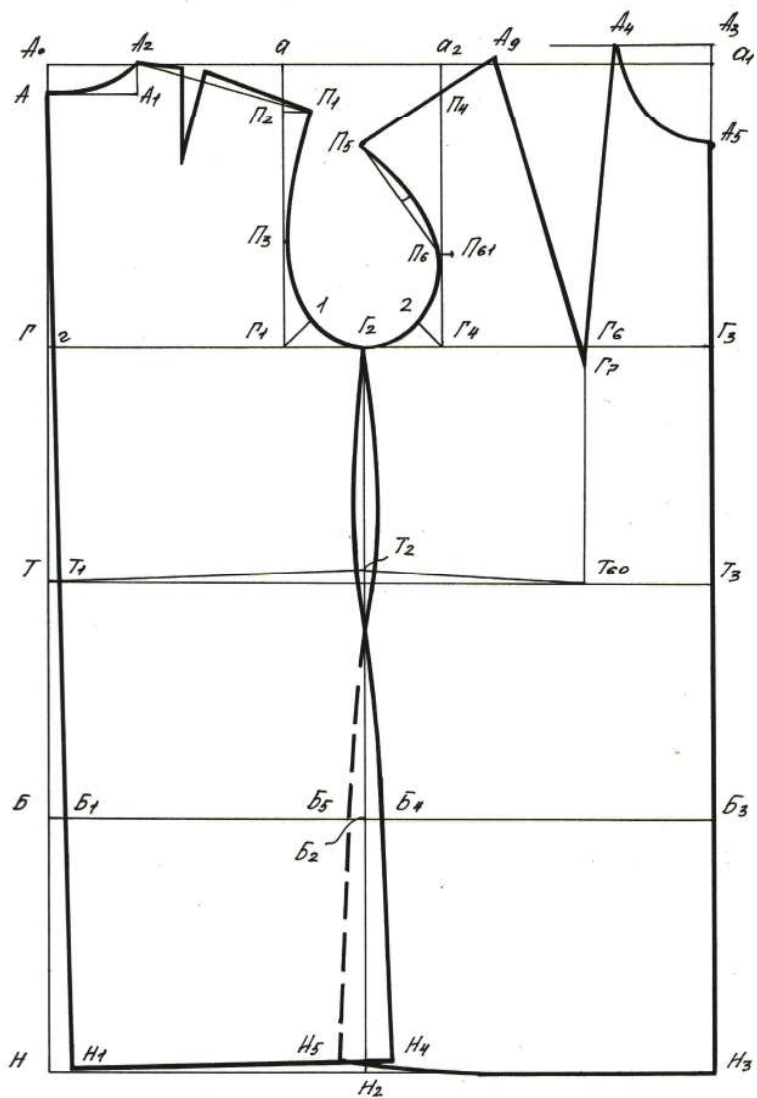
Чертеж конструкции платья прямого силуэта с криволинейным оформлением бокового шва
